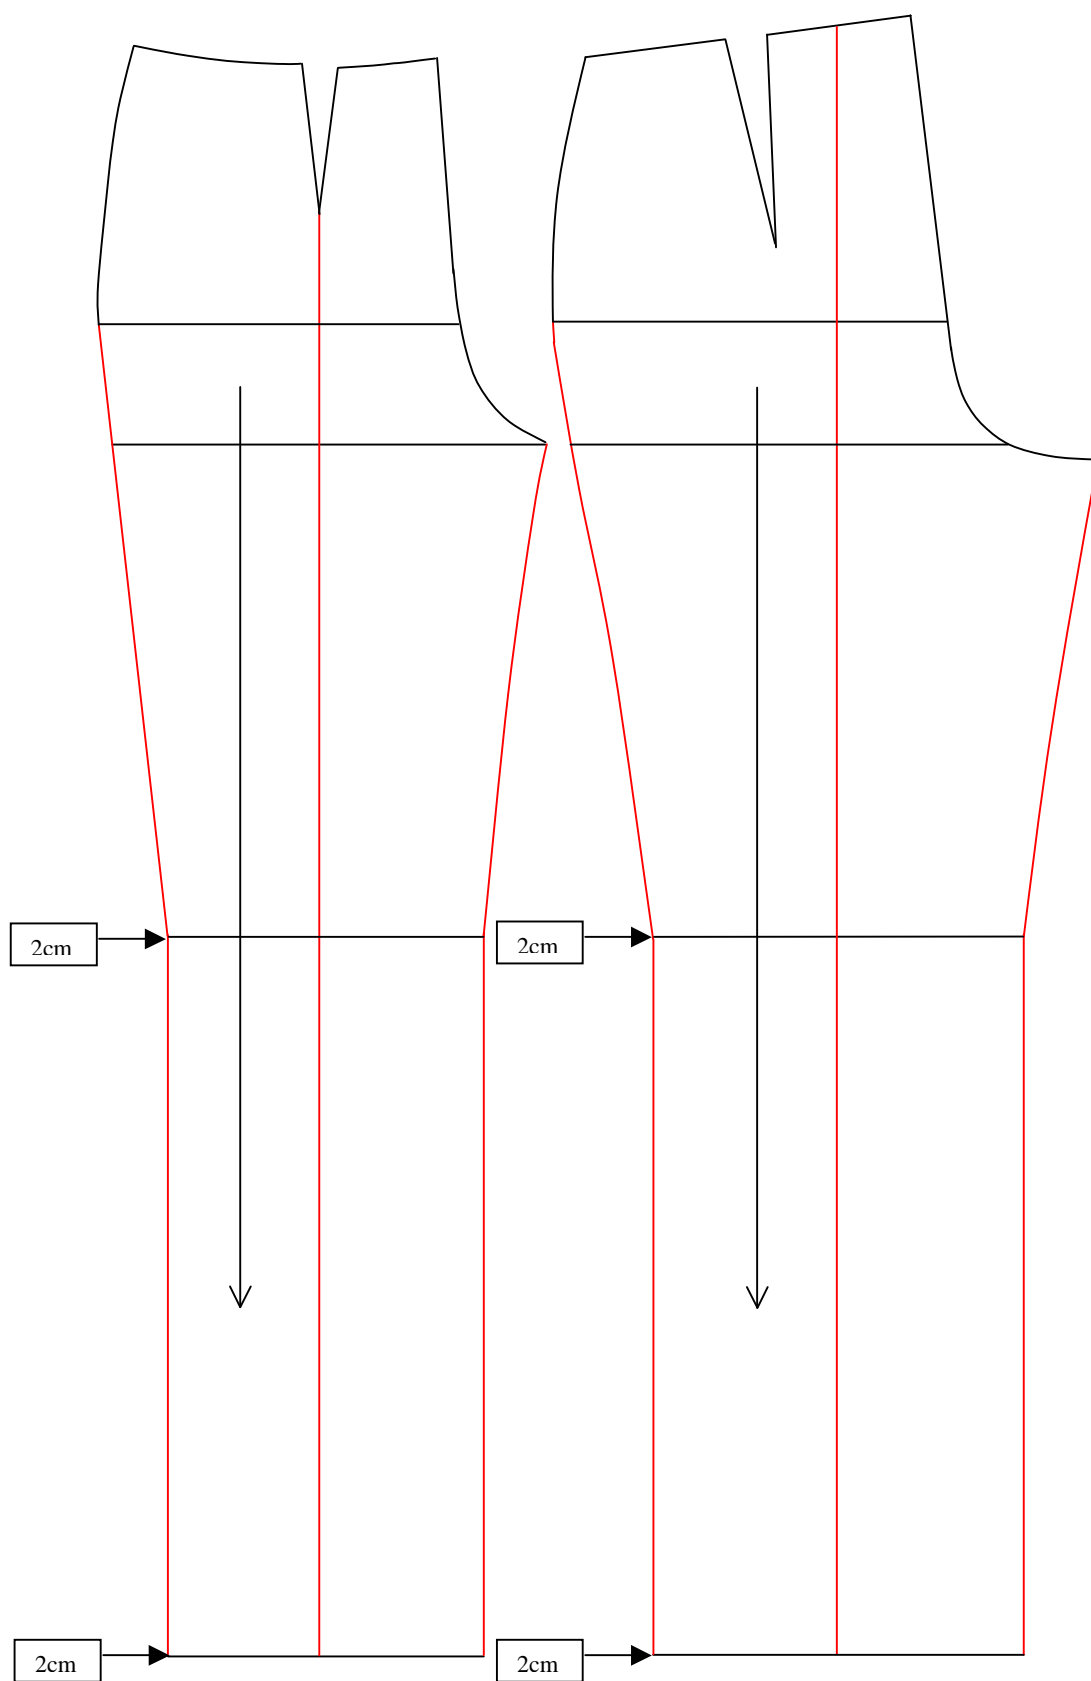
Vbočená kolena PD, ZD – německá metodika 3, vykreslení kalhot a rotace dílů podle směru osnovy
